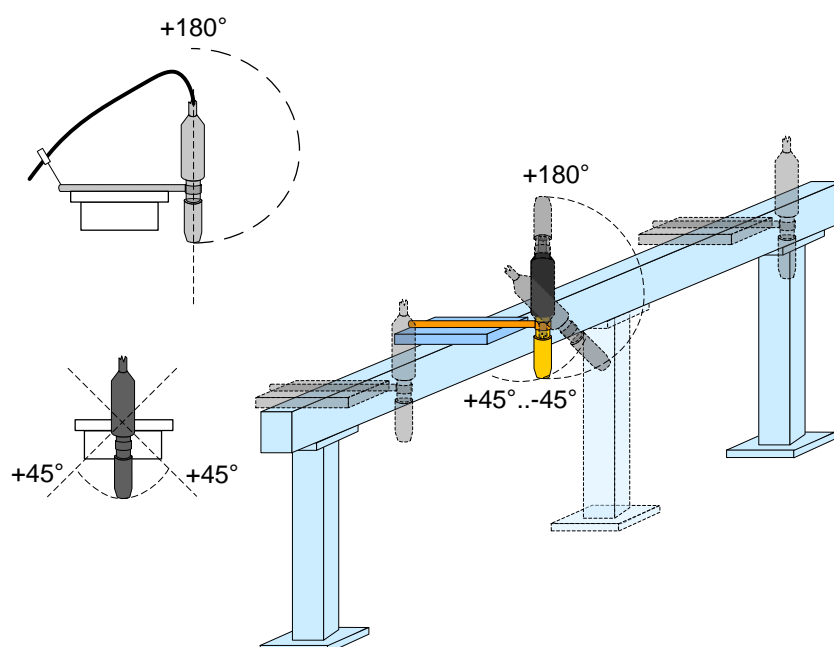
Условная схема конструкции сварочной консоли
